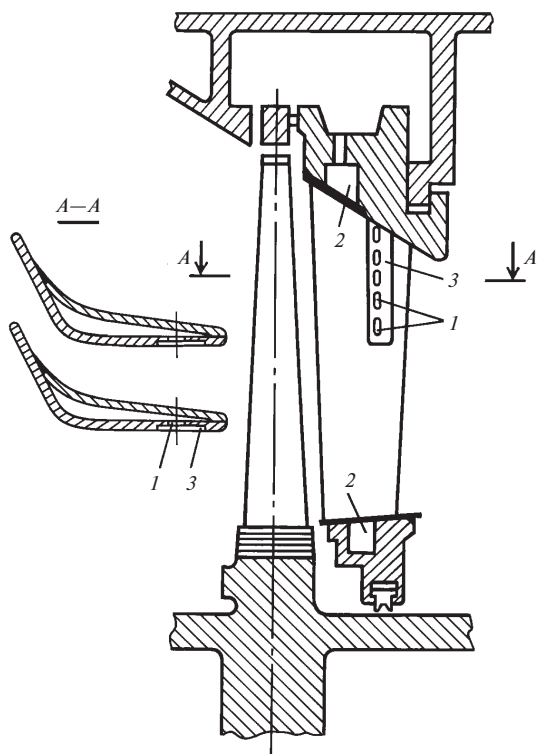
Сварно-штампованная сопловая лопатка ХТЗ (сечение лопатки)
